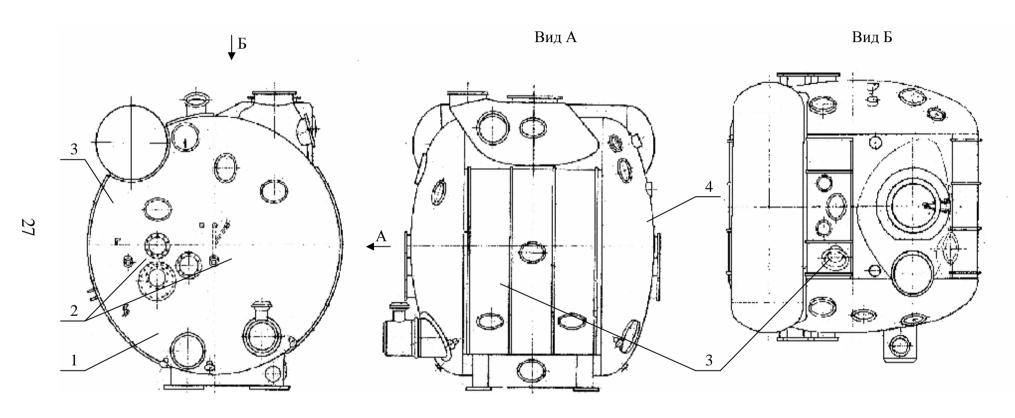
Наружный кожух котла: 1 – днище переднее; 2 – патрубок смотрового устройства; 3 – обечайка; 4 – днище заднее
